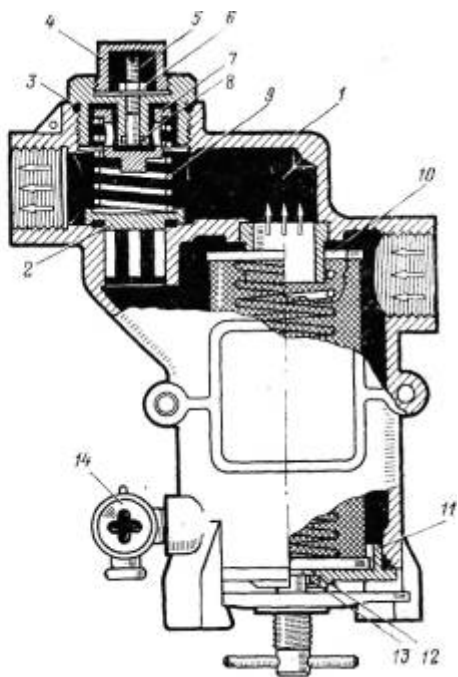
Фильтр тонкой очистки топлива 12ТФ29-1: 1 — корпус; 2 —
